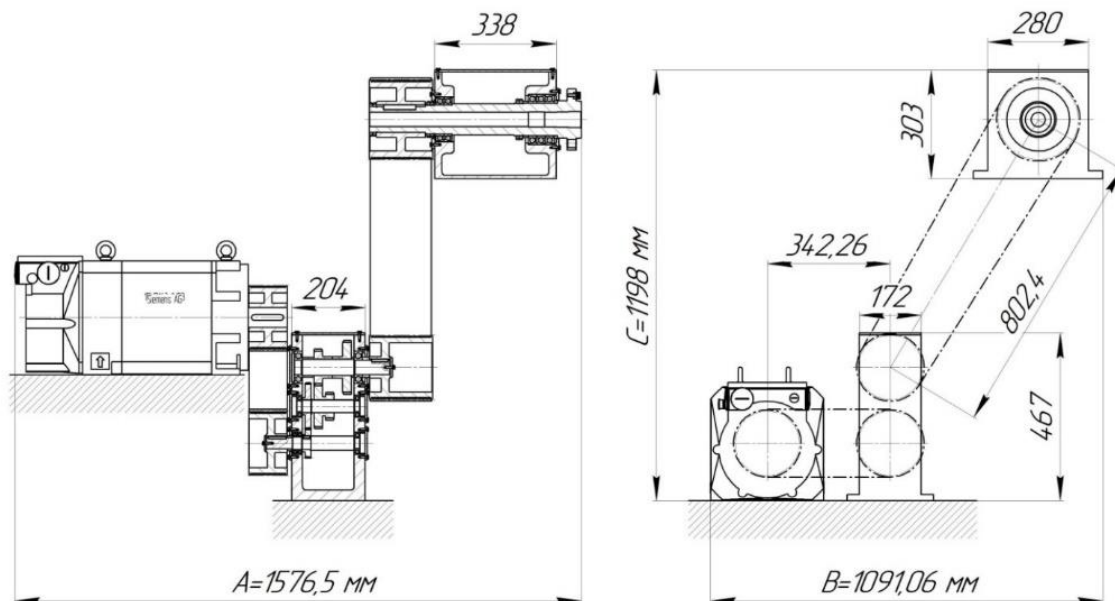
Габаритные размеры привода главного движения варианта компоновки № 1
